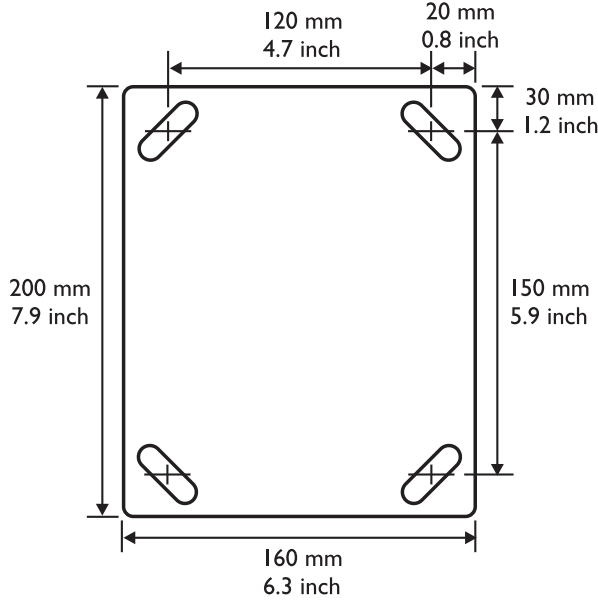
Duvara montaj braketinin duvara takılması
